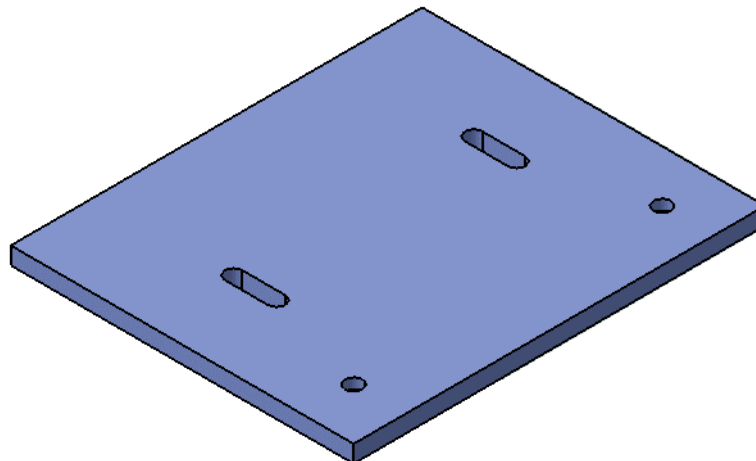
Vista 3D del diseño del ajustador horizontal. Fuente: elaboración propia.
